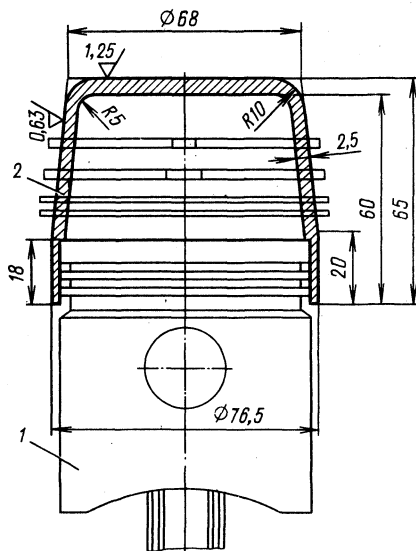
Установка поршневых колец на поршень двигателя МеМЗ:
